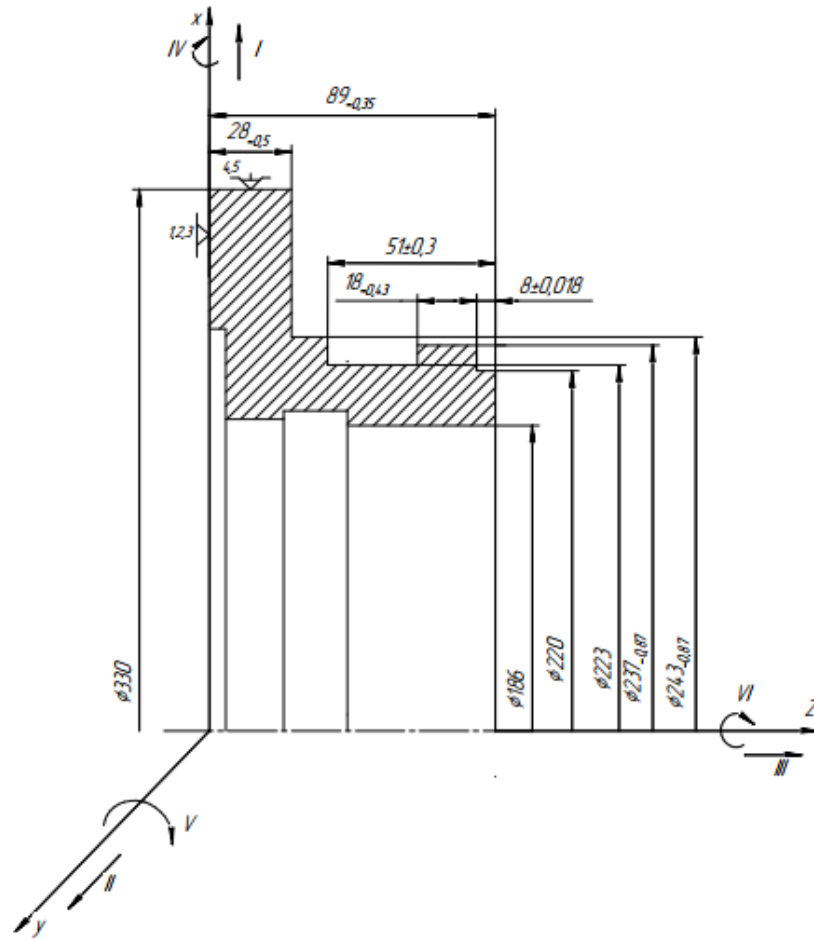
Схема базування заготовки по діаметру 330 мм і прилеглому торцю $28_{-0,5}$ мм
